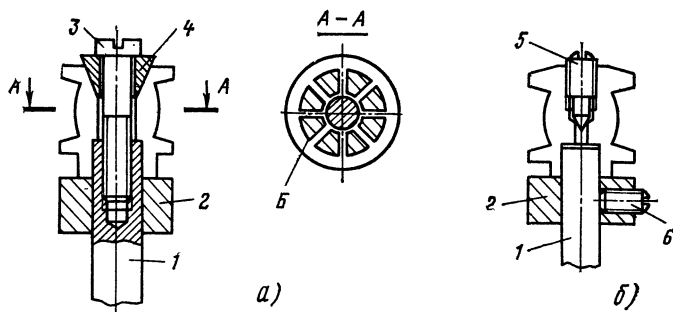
Примеры конструкции ведущего шкива (насадки), позволяющей регулировать его диаметр.
